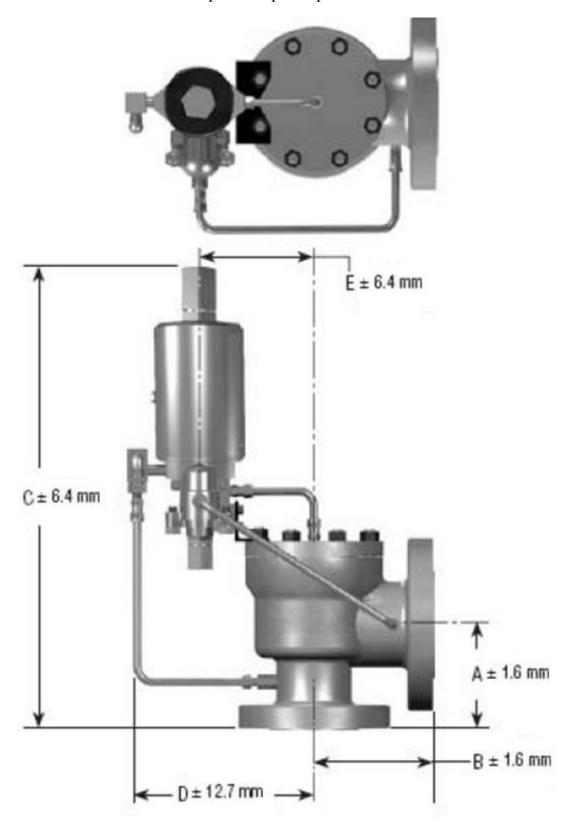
Габаритные размеры клапана предохранительного со стандартным проходным сечением
